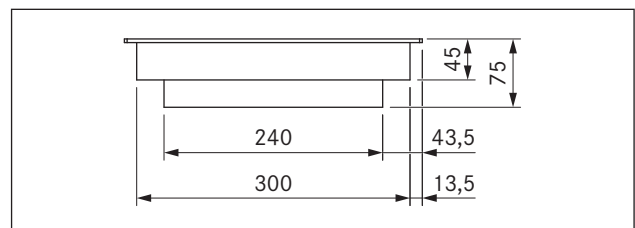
CKCB apparatets dimensjoner sett forfra
